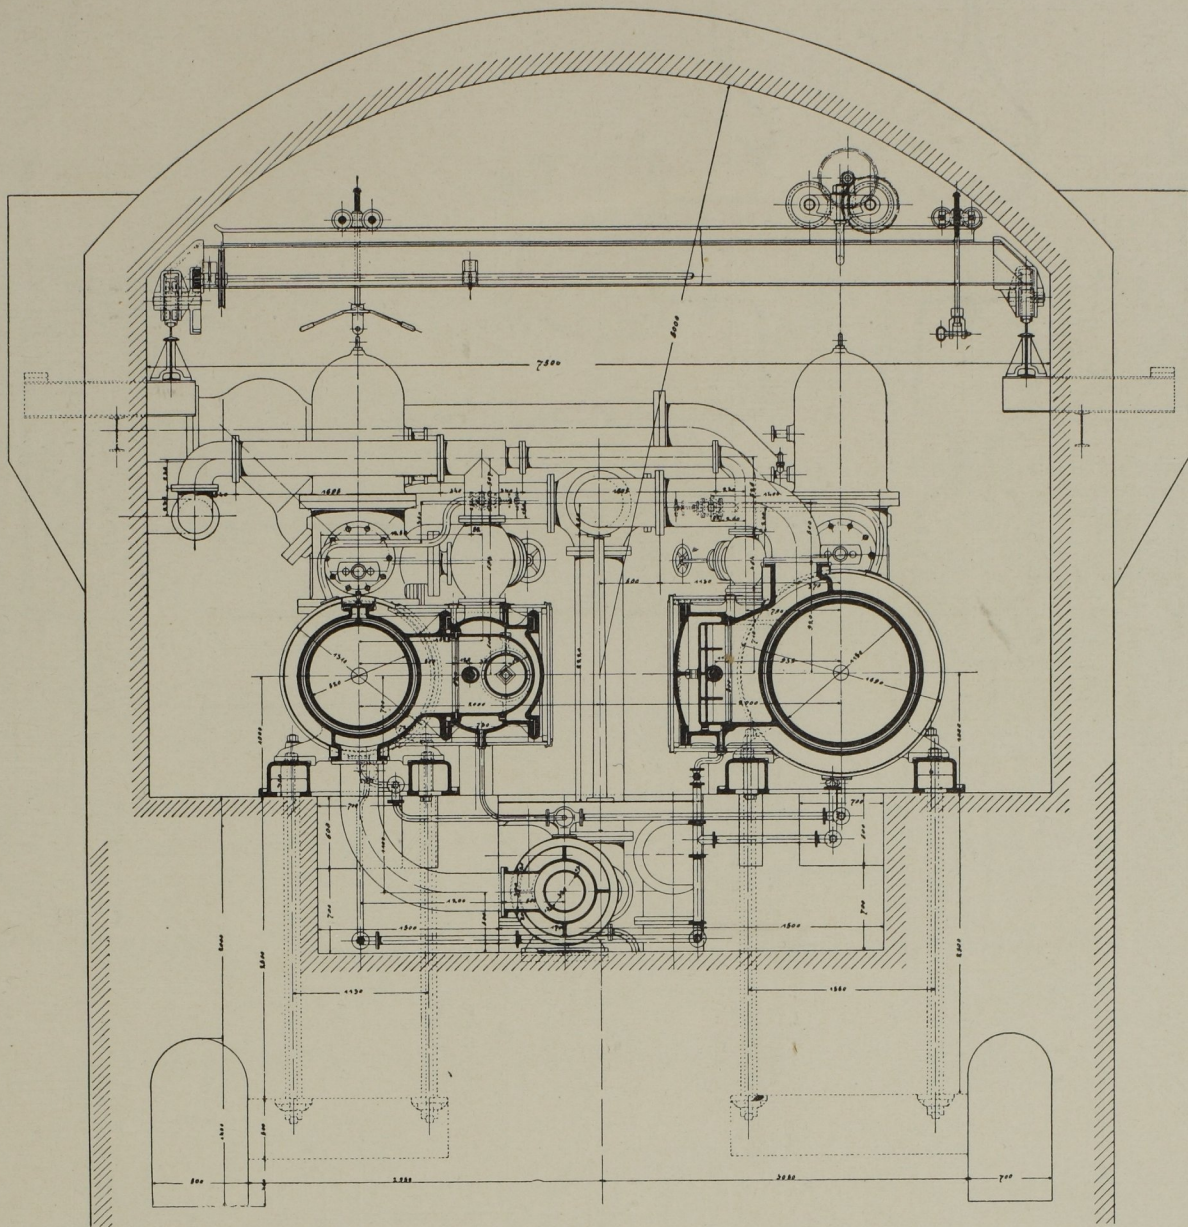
Querschnitt durch die Dampfzylinder. Masst. 1:60.
